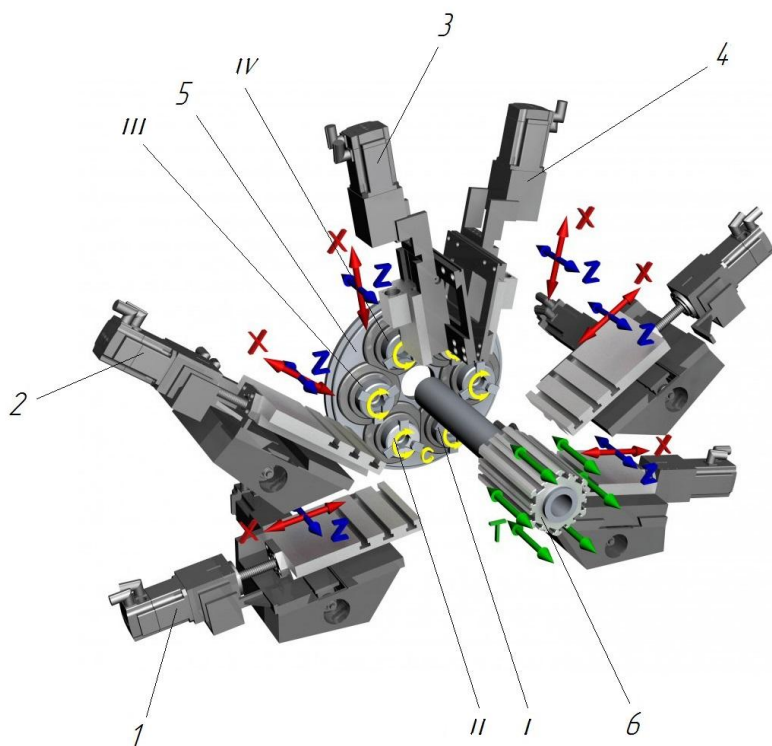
Четырехшпиндельный токарный полуавтомат
